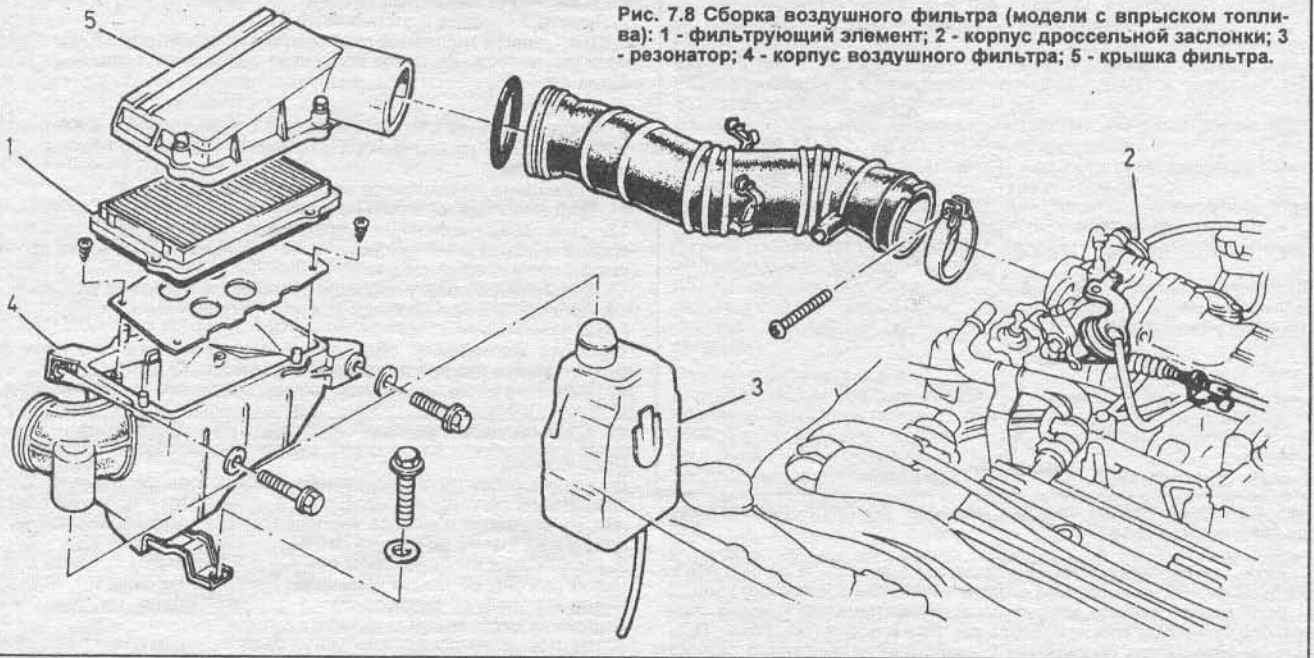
Сборка воздушного фильтра (модели с впрыском топлива): 1 - фильтрующий элемент; 2 - корпус дроссельной заслонки; 3 - резонатор; 4 - корпус воздушного фильтра; 5 - крышка фильтра.
